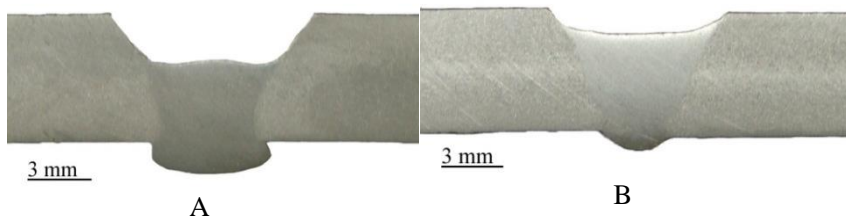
Secção transversal das soldagens mecanizadas com $v = 40$ cm/min e $V_a = 7,0$ m/min, em: A – MIG Convencional, B – MIG CMT
